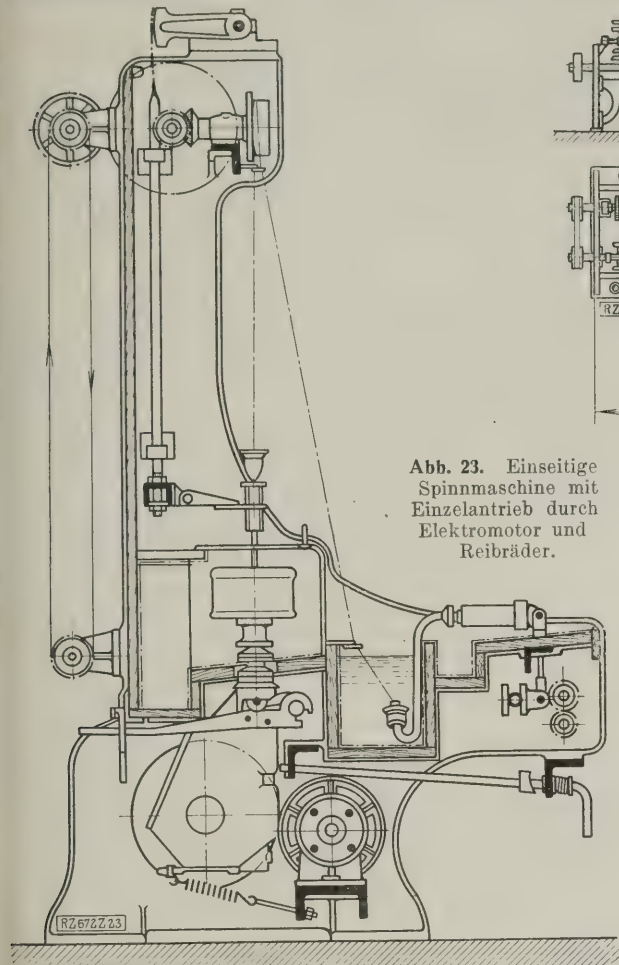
Einseitige Spinnmaschine mit Einzelantrieb durch Elektromotor und Reibräder.
